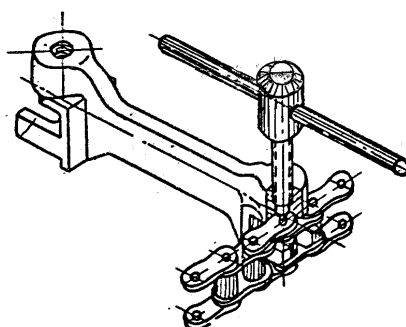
Приспособление для разборки втулочно-роликовых цепей
